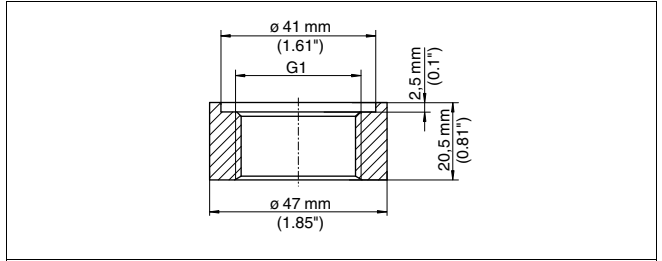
Maße Einschweißstutzen G1 A nach DIN 3852-X
